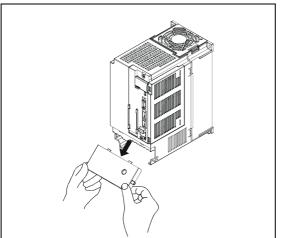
Schritt ③: Entfernen der Frontabdeckung
